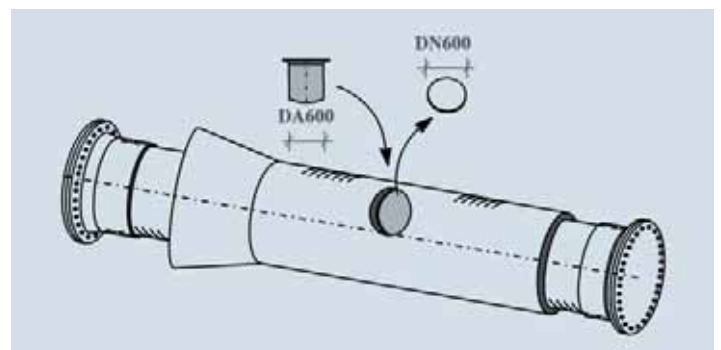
Einschweißen des PE-Lüftungsstutzens
